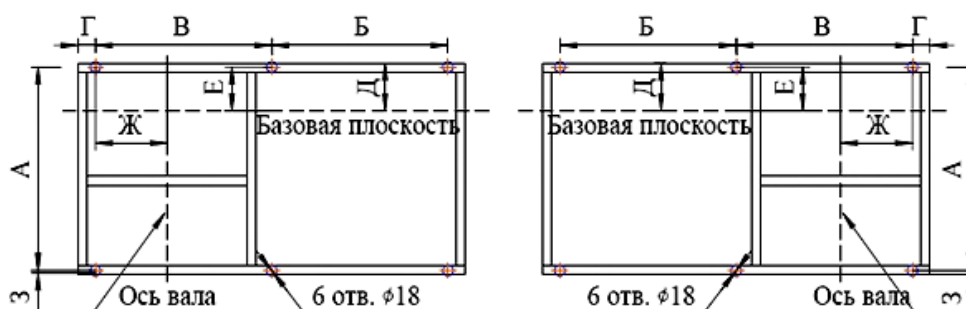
Вентиляторы ВРП-115-49-8. Установочные размеры (вид снизу на основание вентилятора).
